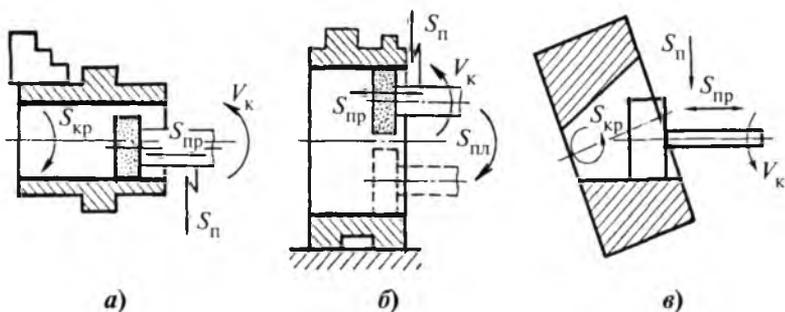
Схемы обработки заготовок на внутришлифовальных станках:
